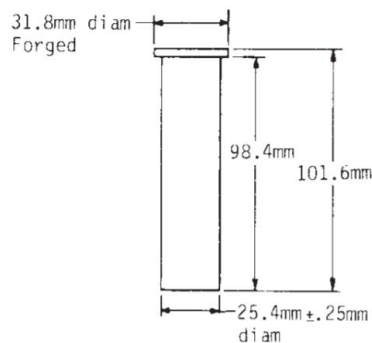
Especificações dimensionais de corpo de prova forjado para ensaio Jominy, segundo ASTM A255. Fonte: [55].
